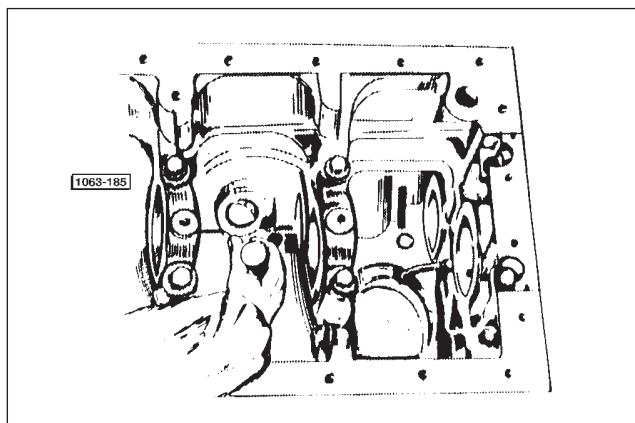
Après graissage à l'huile moteur, mettre le plaquettes des poussoirs dans leurs portées au bloc-moteur.
